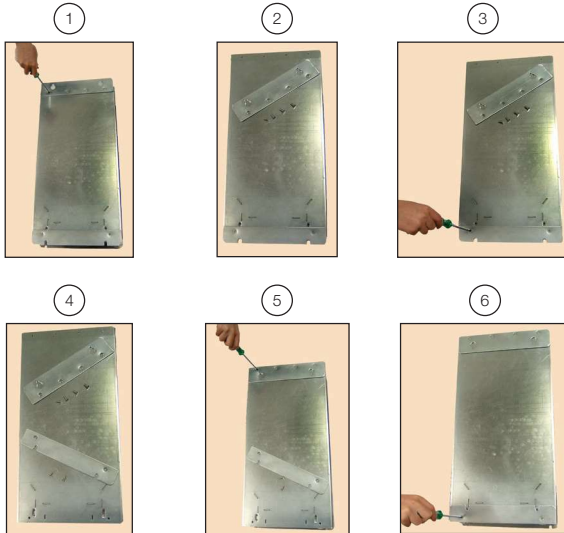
Reposicione os suportes de montagem nas mecânicas A a E. Nas mecânicas F, G e H os suportes devem ser removidos
